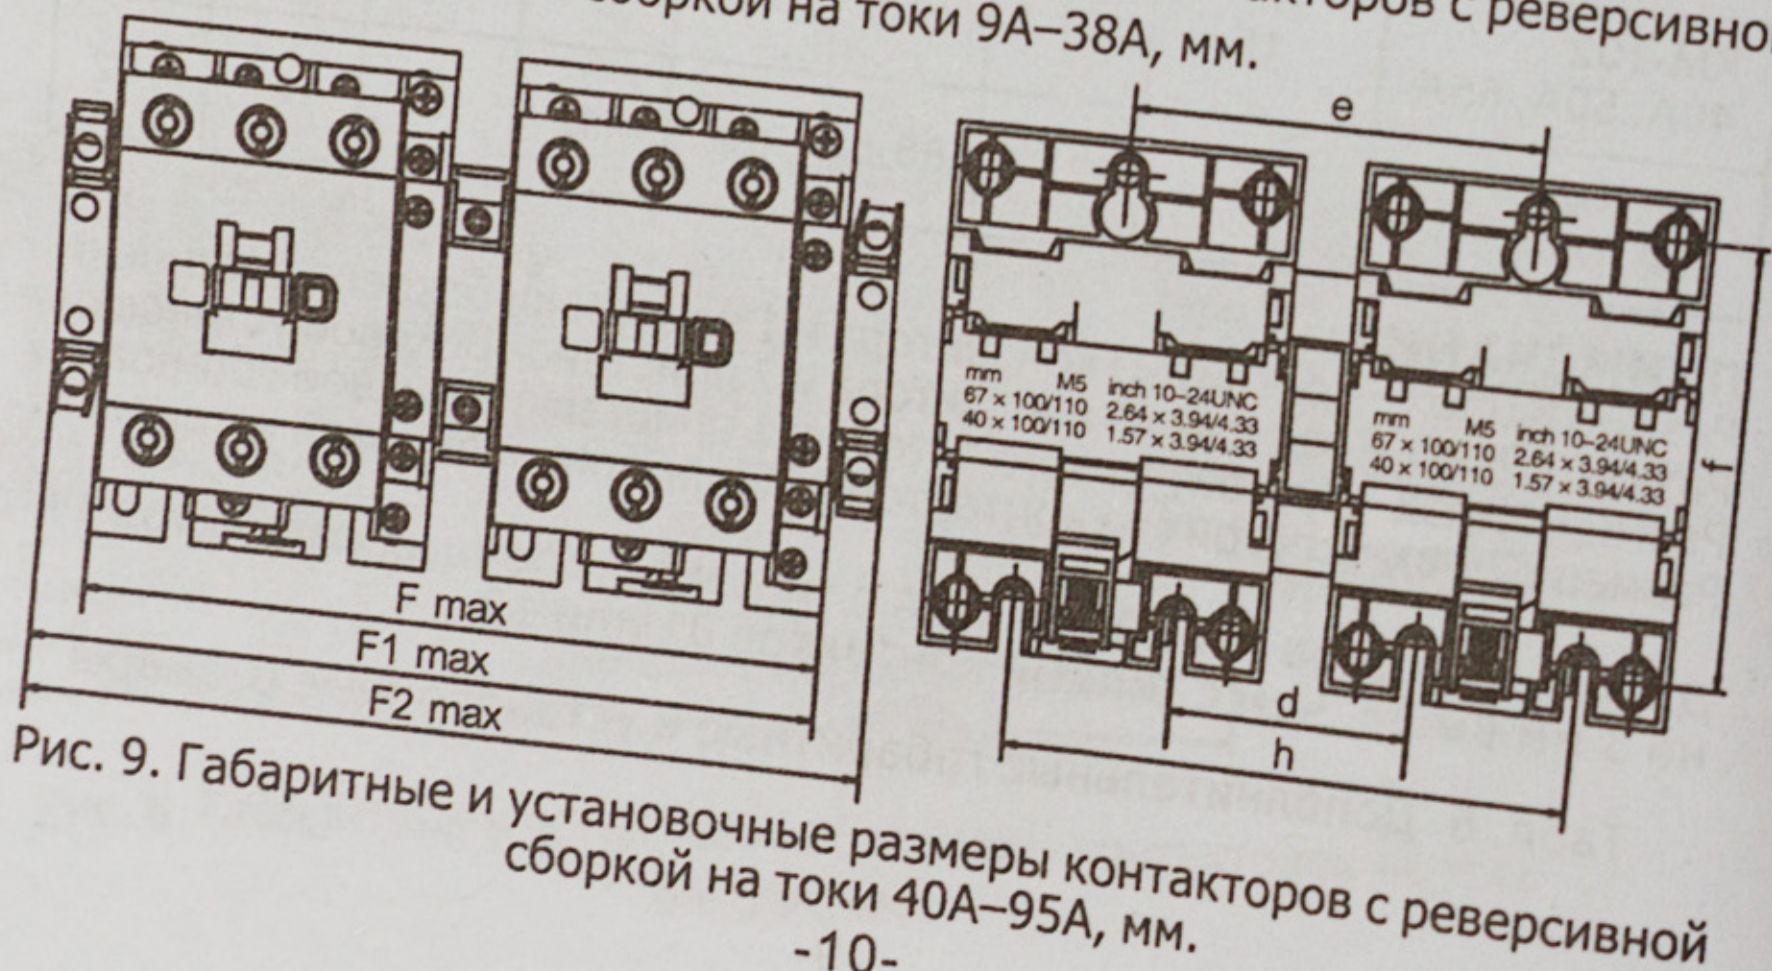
Габаритные и установочные размеры контакторов с реверсивной сборкой на токи 40А–95А, мм.
